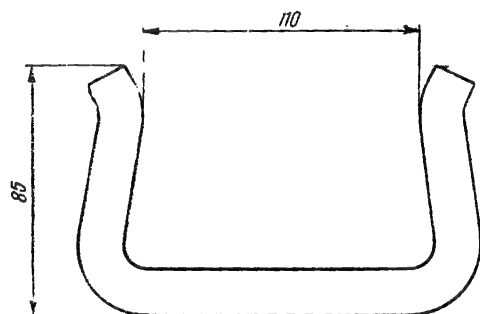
Clemă de asamblare din oțel-rotund Ø 18 mm.
